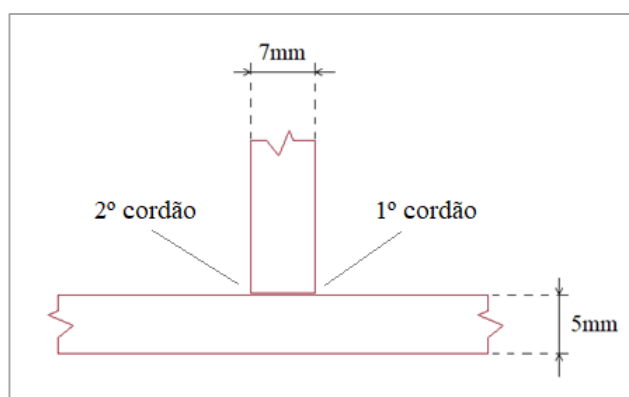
Junta de soldadura de canto (Fonte West-sea)
